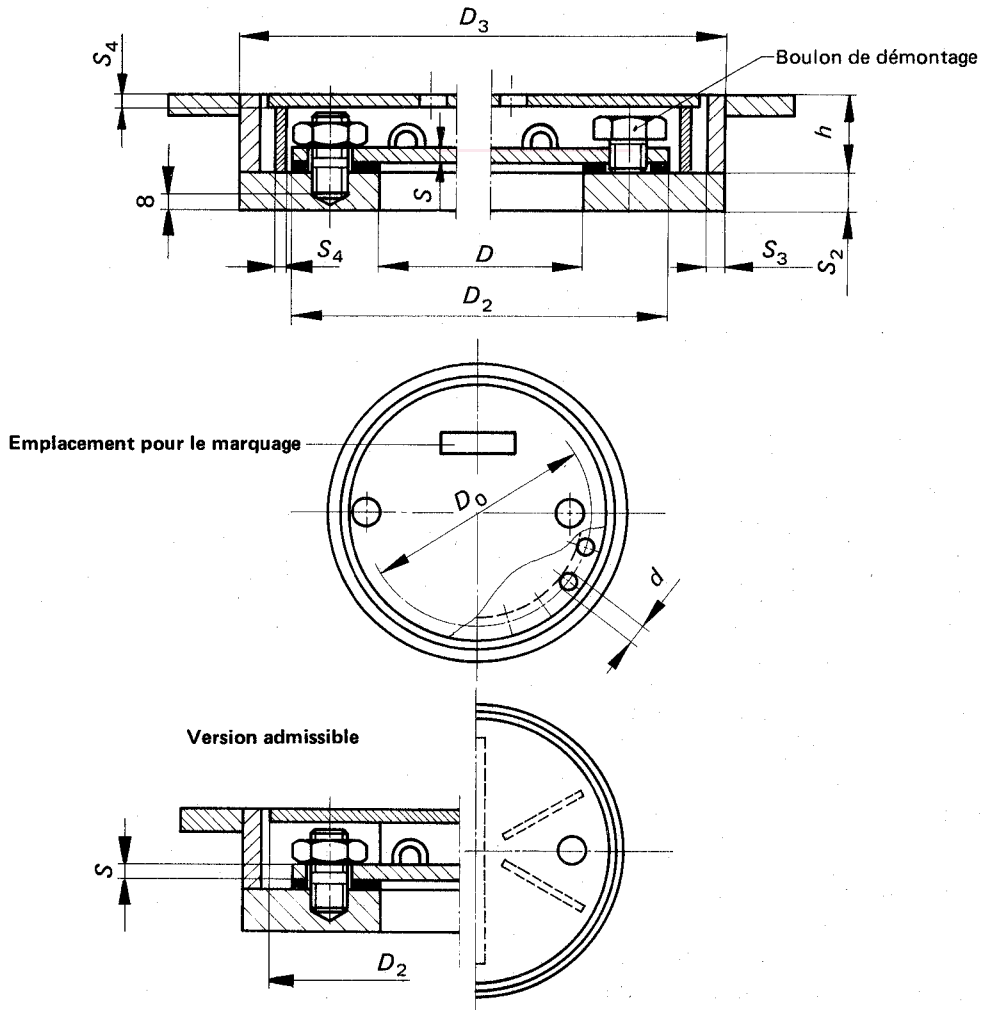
Forme et dimensions principales des trous d'homme, type B
